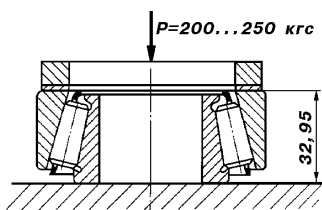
Замер монтажной высоты подшипника ведущей шестерни главной передачи
